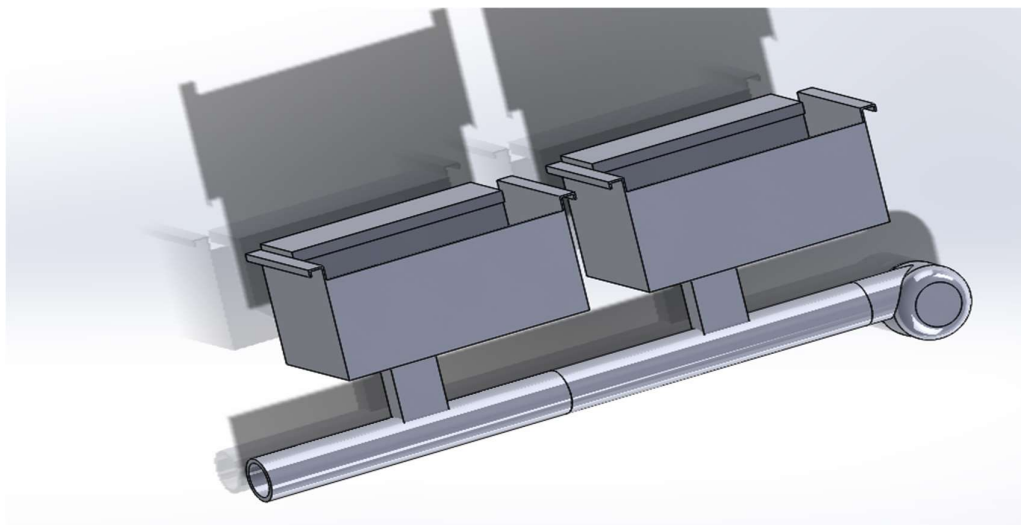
Vue de face de la table aspirante placée au-dessus du bac.
